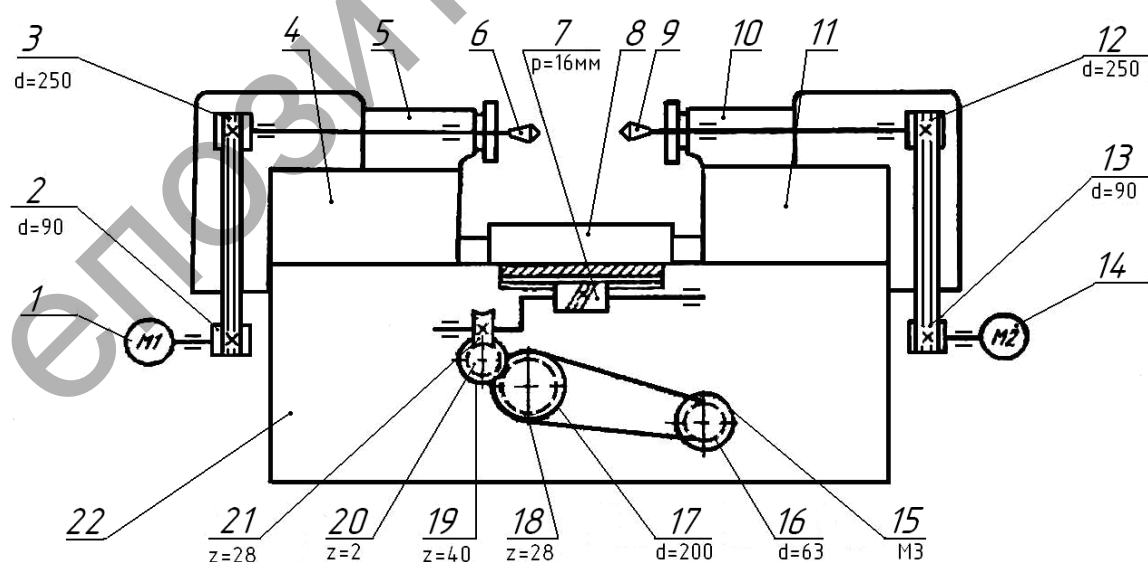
Устройство горизонтального алмазно-расточного станка модели 2712А
